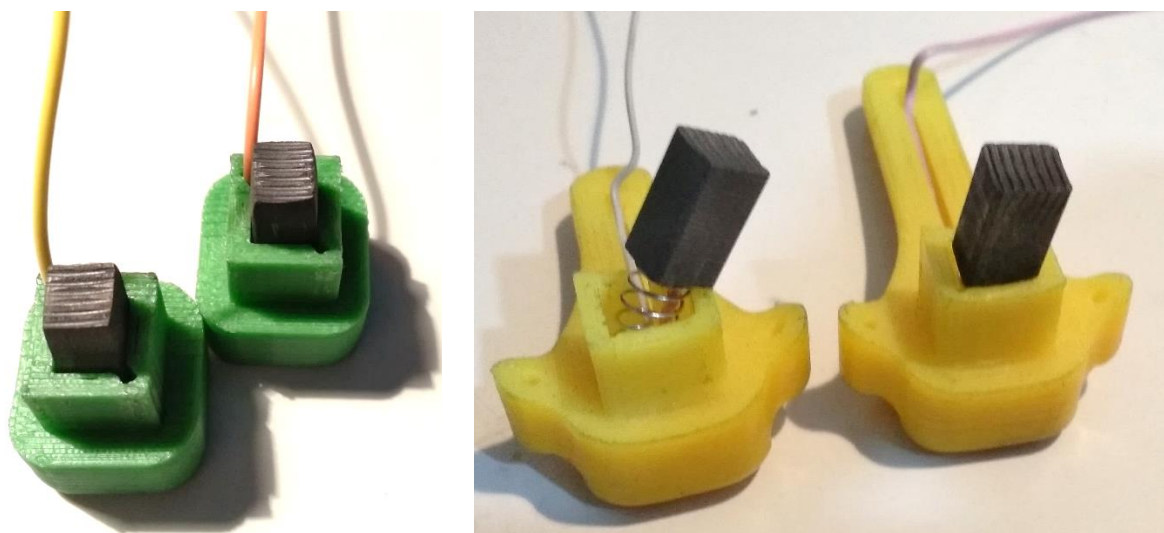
Montaje de escobillas. (Izquierda) primer prototipo. (Derecha) prototipo final.
